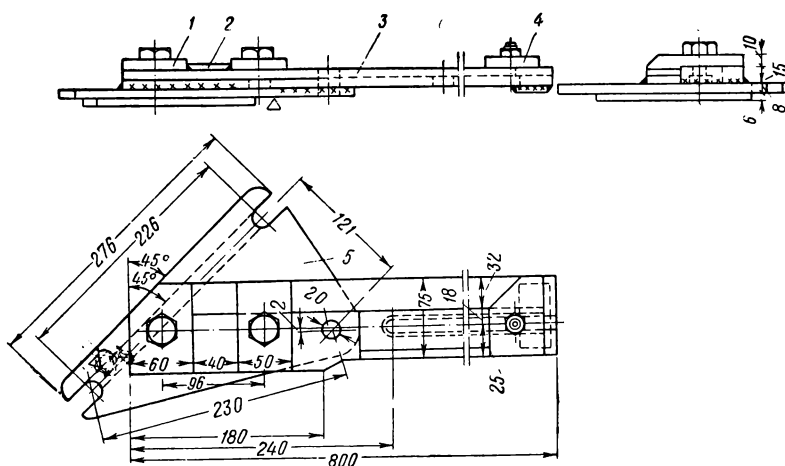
Приспособление для нарезки накладок на фрезерном станке:
